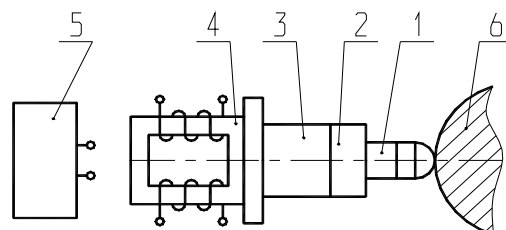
Схема ультразвуковой установки с деформирующим инструментом в виде полусферы: 1 – деформирующий инструмент; 2 – концентратор УЗК; 3 – волновод; 4 – преобразователь УЗК; 5 – генератор; 6 – обрабатываемая деталь.
